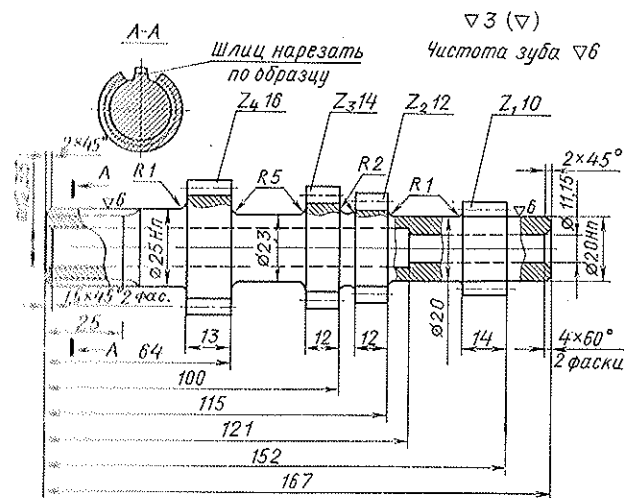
Валы и шестерни к спортивной коробке передач. Первичный вал. Данные для изготовления шестерен первичного вала:
